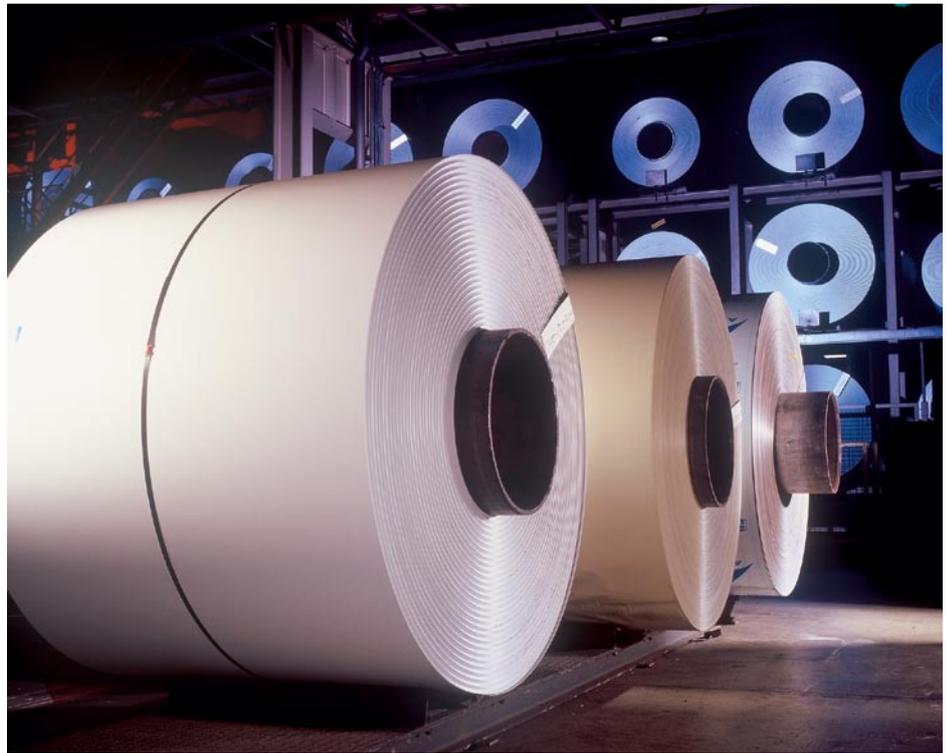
Aluminium-Großcoils mit einem Stückgewicht bis zu 10 t.
